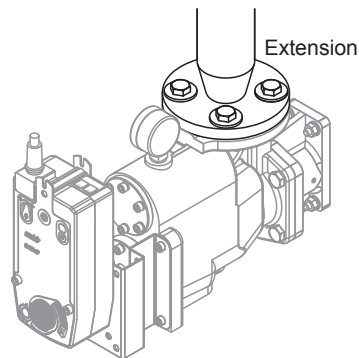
Extension de la conduite d'alimentation en vapeur
